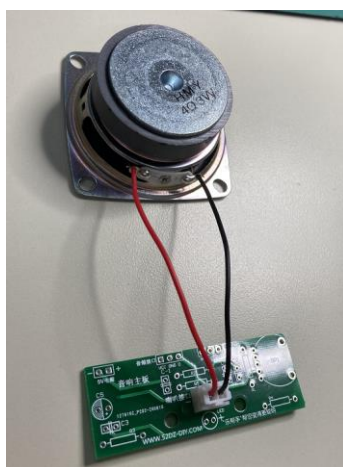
喇叭与音箱主板 PCB 使用电源线连接
